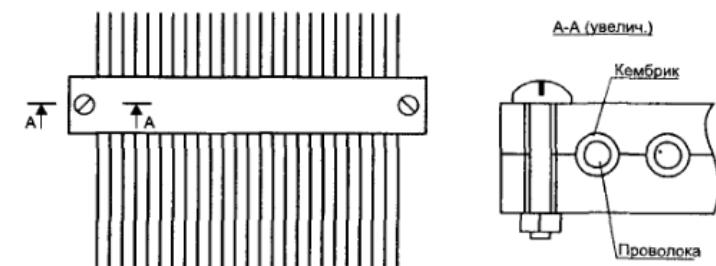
Приспособление для копирования криволинейных поверхностей
